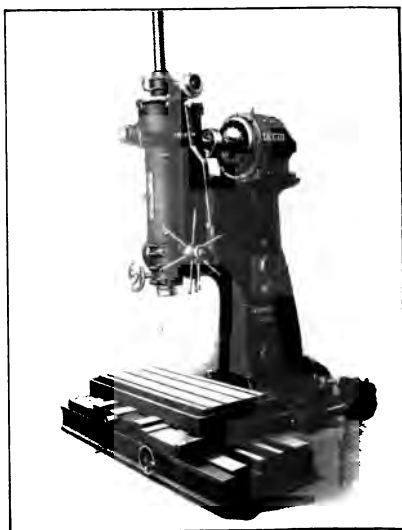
Máquinas de taladrar con motor regulable de eje horizontal.
